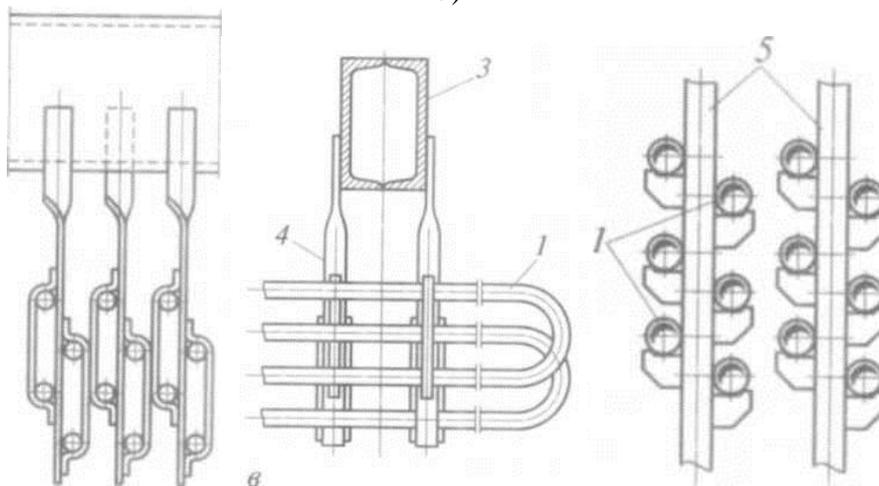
Крепление вертикальной (*а*), горизонтальной (*б*) и потолочных труб (*в*) пароперегревателя (треугольником указаны места сварки)
